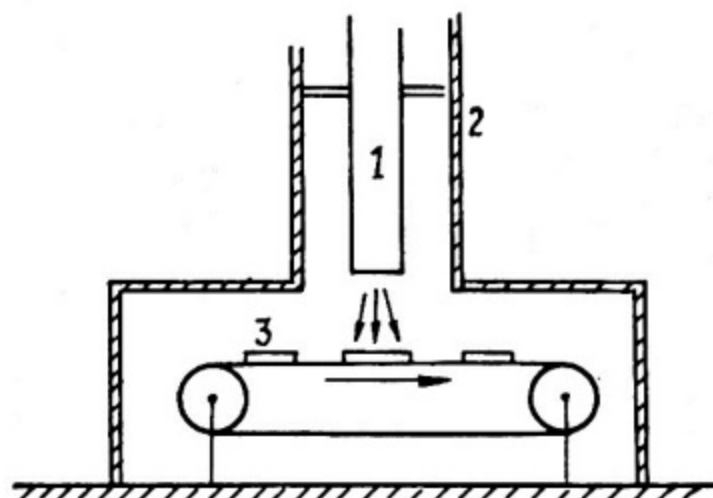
Схема установки для отверждения лакокрасочных покрытий:
